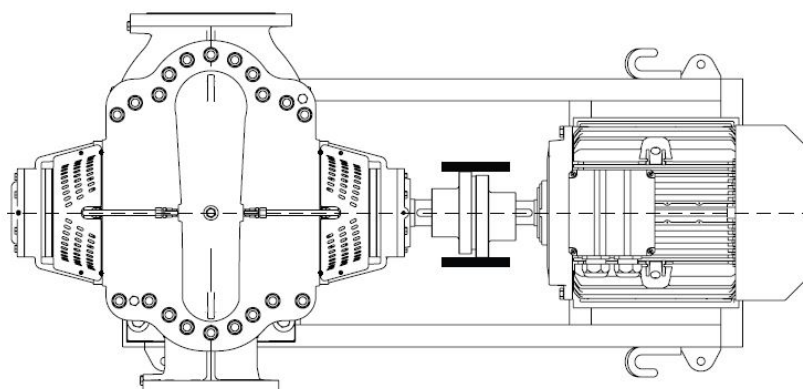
Achados não coaxiais na aplicação do plano horizontal
